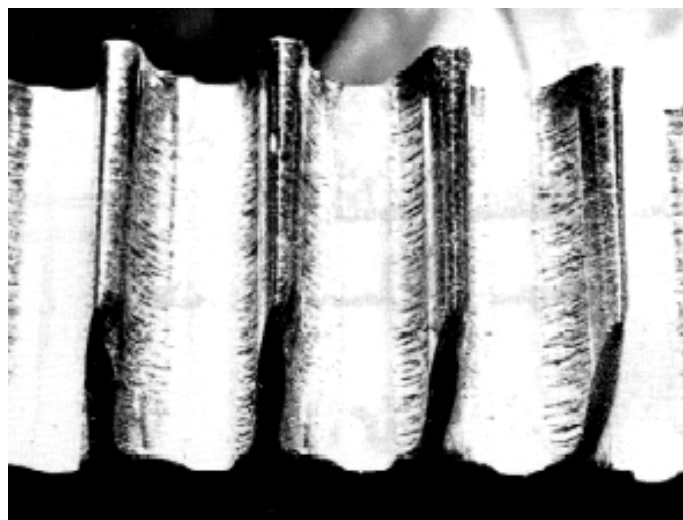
Desgaste abrasivo severo, nos dentes de uma engrenagem [31].
